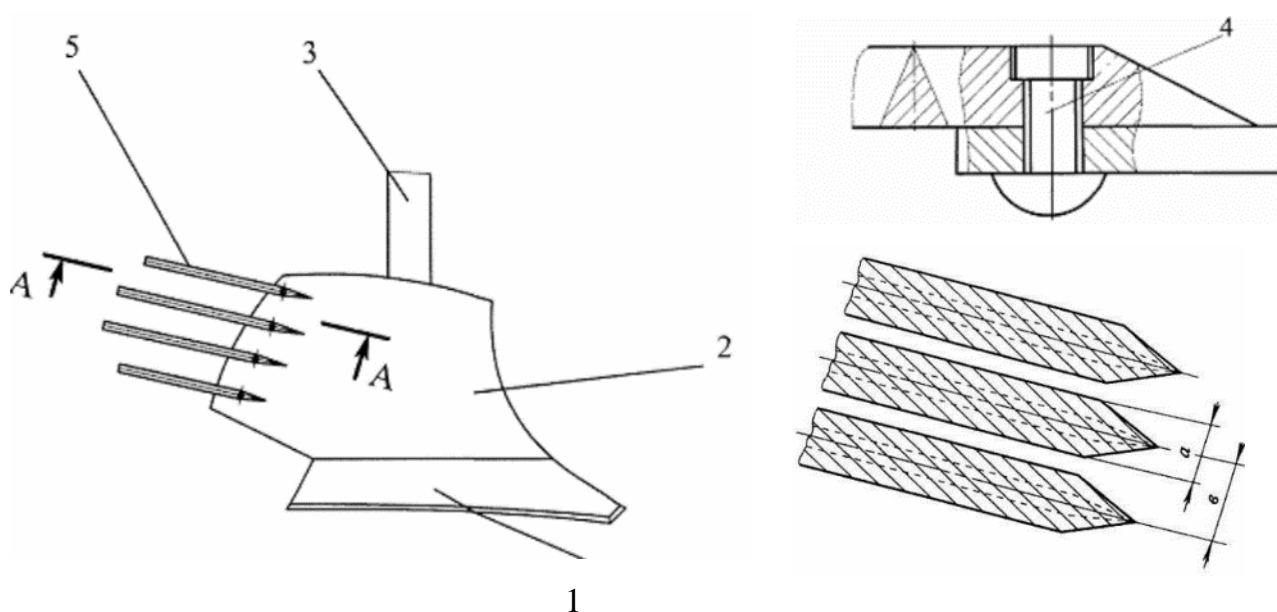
Корпус плуга з пластинами-ножами [110]
